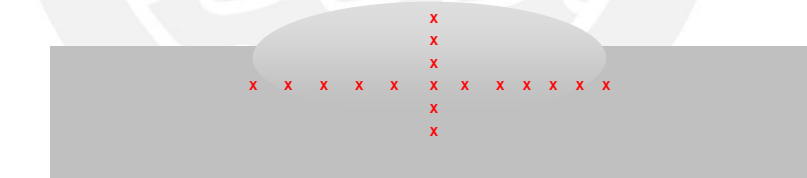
Esquema del barrido de durezas horizontal y vertical
